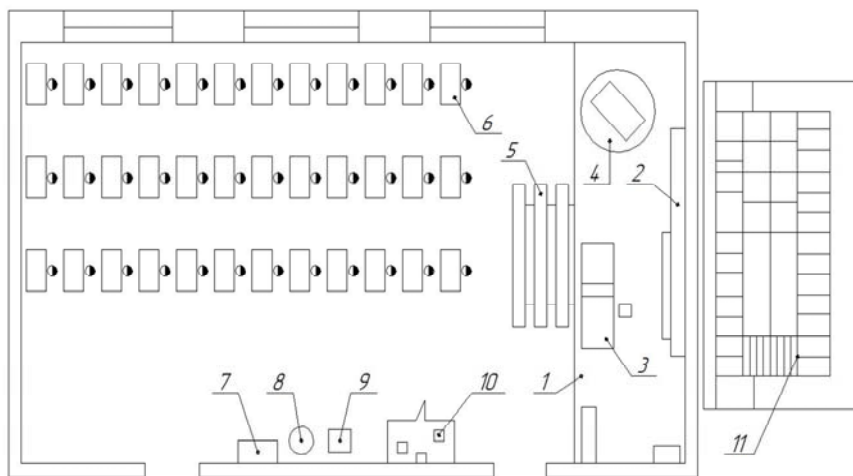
Схема фронтальной планировки слесарной мастерской:
